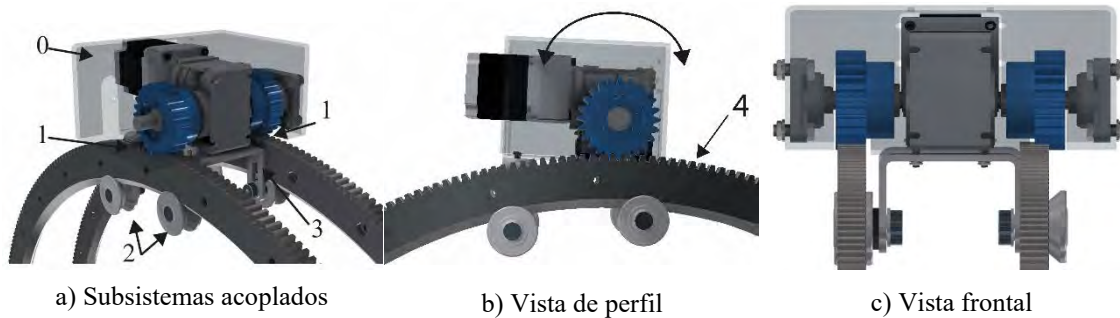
33 Ensamble del tractor soldador y el sistema de sujeción
